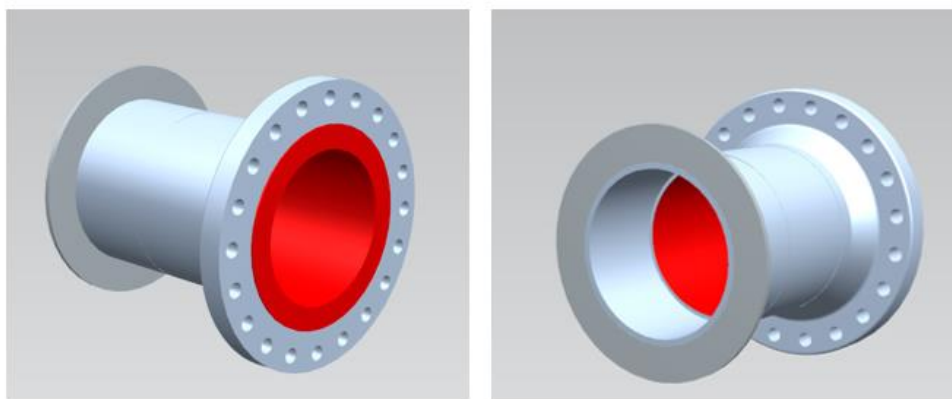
Tubuladura formada por una brida, un tubo y un refuerzo
